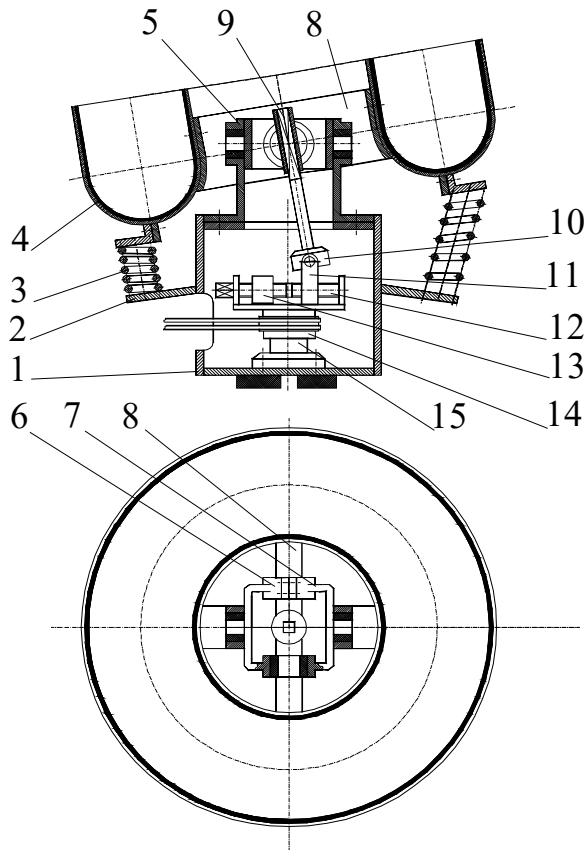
Конструктивна схема вібраційно-відцентрової установки ВВУ II
